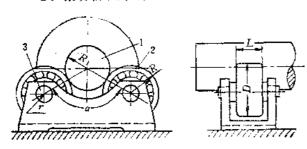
滚动输承式静平衡装置 1-零件轴颈 2-轴承 3-心轴
